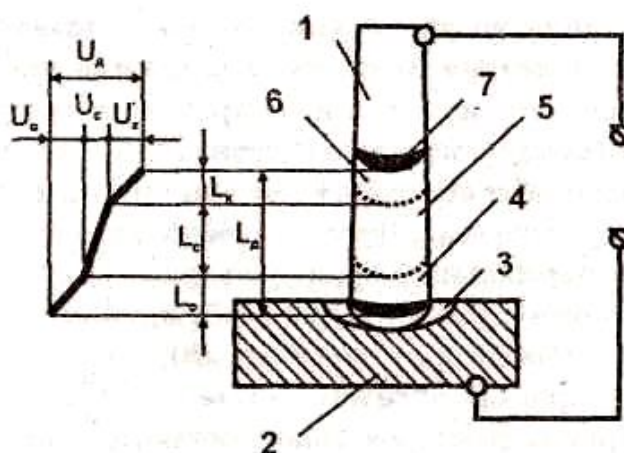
Схема сварочной дуги и падения напряжений в ней:
